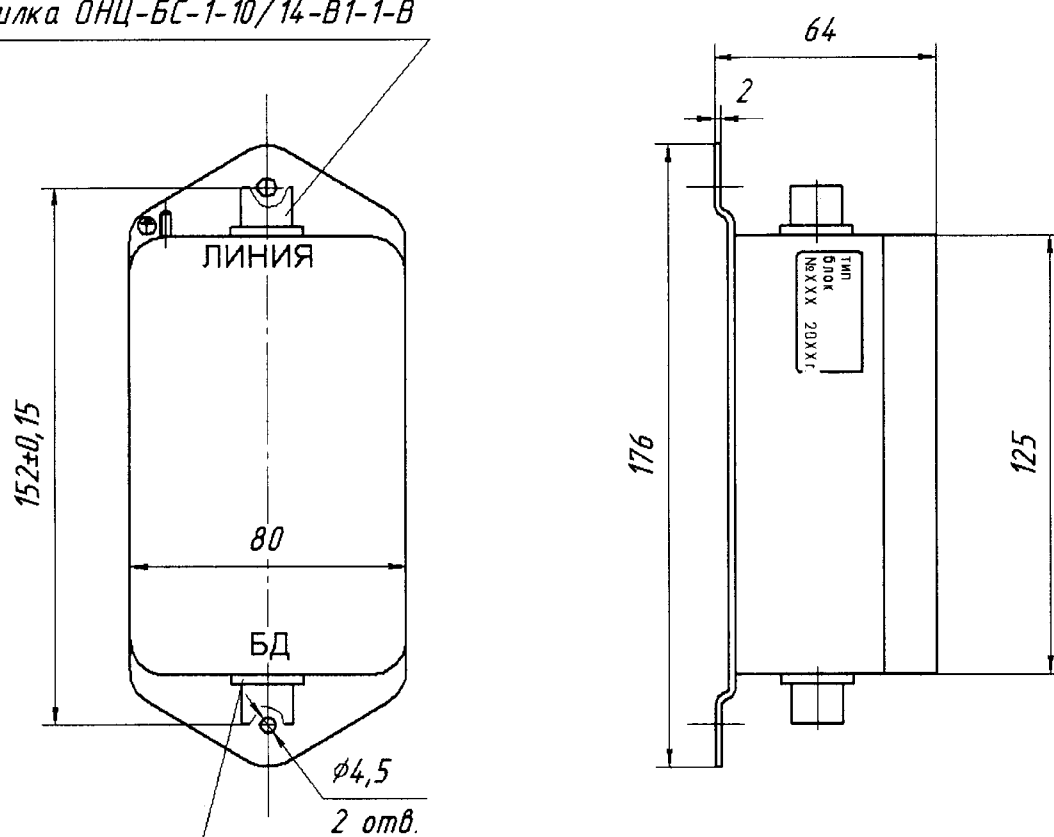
Габаритные и присоединительные размеры блока БСПП-16д
